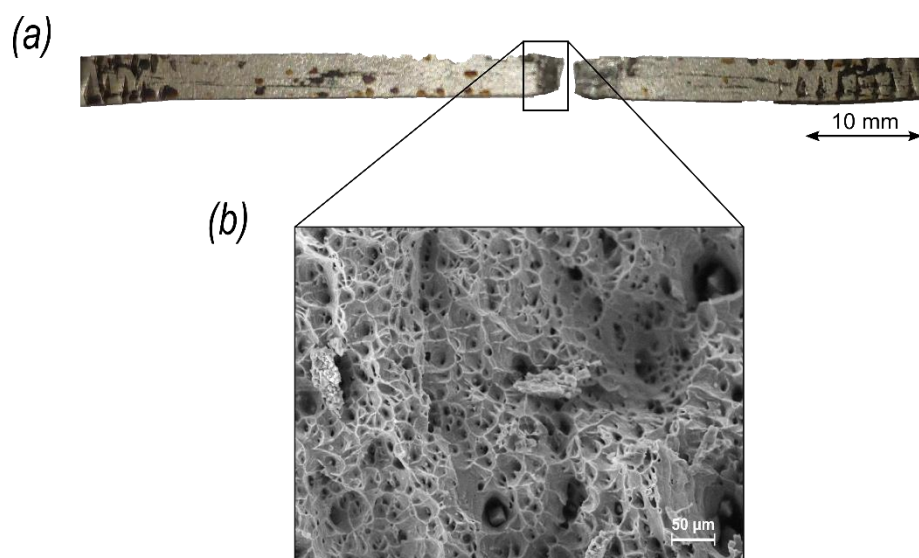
(a) #4_LAE_1_1000°C_1H após ensaio de tração uniaxial. (b) Superfície de fratura.
